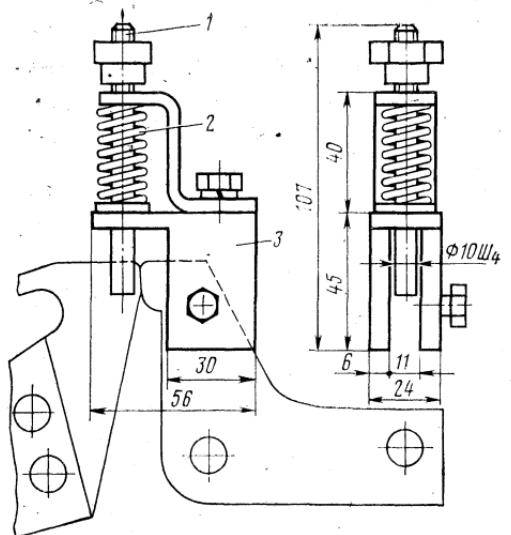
Приспособление для определения отброса подвижного контакта быстродействующего выключателя от буфера
